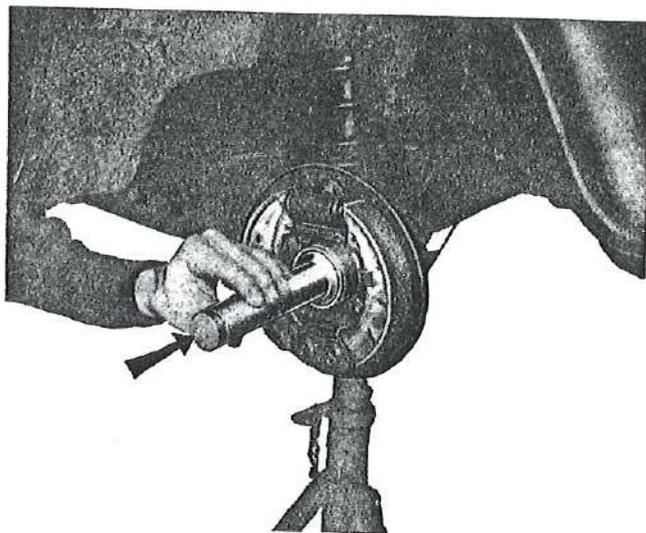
Montaje de los anillos exteriores de los rodamientos a rodillos interior y exterior, mediante el útil A. 66041.
